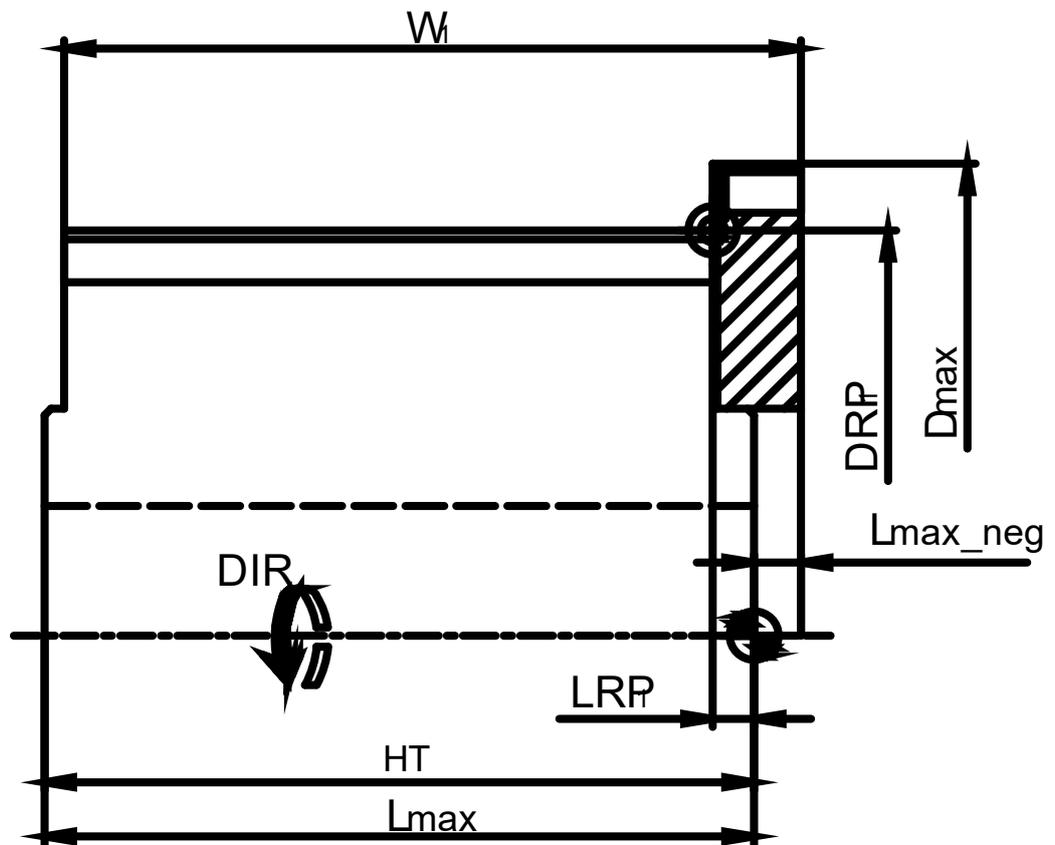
Maßdefinition für HSK-W-Hobelwerkzeuge
